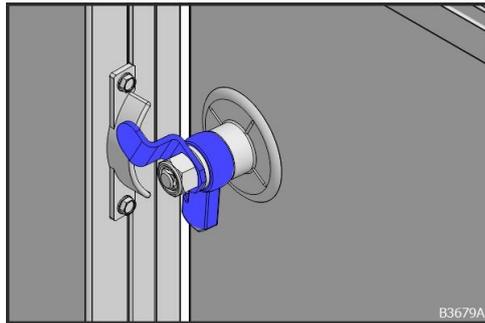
Nockenzunge mit Fanghaken (druckseitig)
